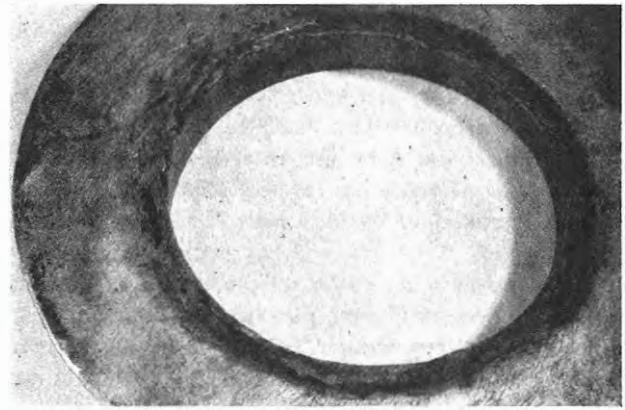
Corrosion électrochimique. Collet en cuivre soudé sur un tube de cuivre. L'attaque s'est produite à la soudure qui est en laiton; le zinc seul s'est dissous et il subsiste du cuivre poreux
